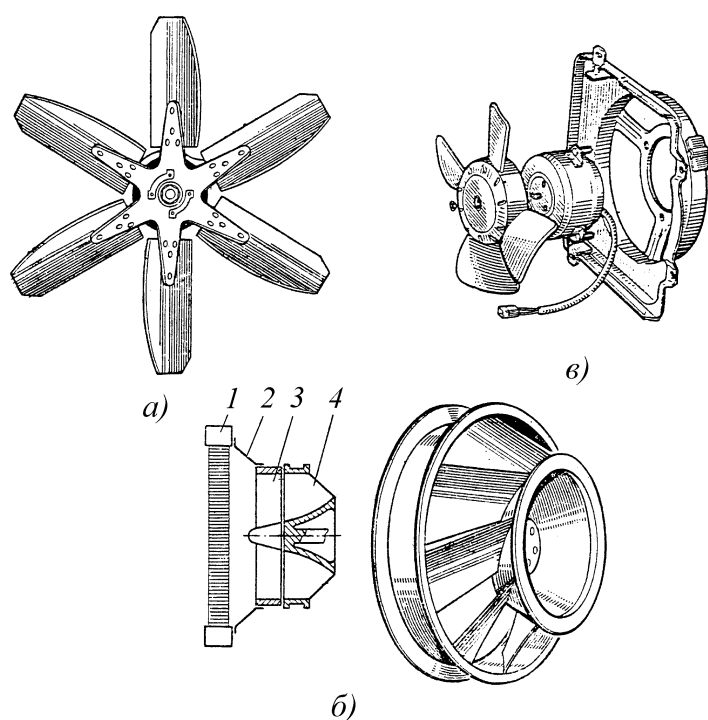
Вентиляторы жидкостной системы охлаждения: а - штампованный стальной; б - литой алюминиевый; в - пластмассовый с приводом от электродвигателя; 1 - радиатор; 2 - кожух; 3 - направляющий аппарат; 4 - вентилятор
